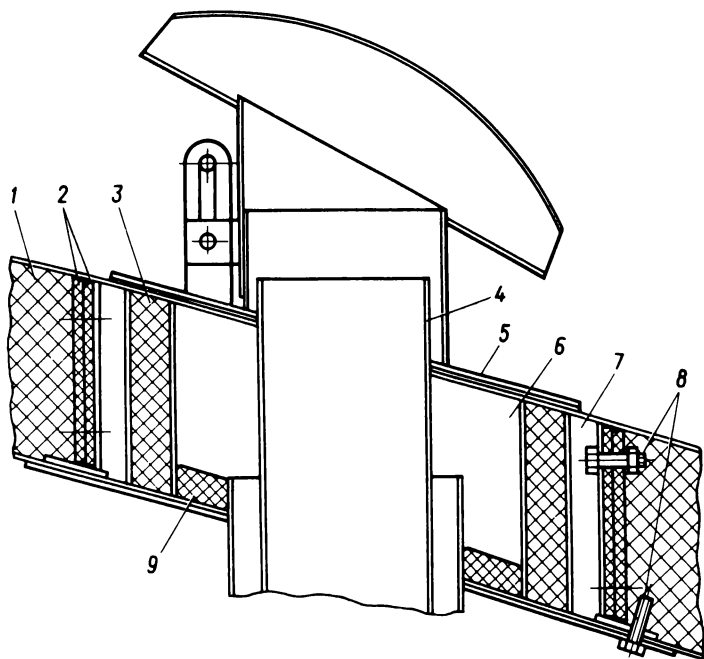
Разделка крыши для дымовой трубы котла системы отопления пассажирского вагона постройки ГДР
